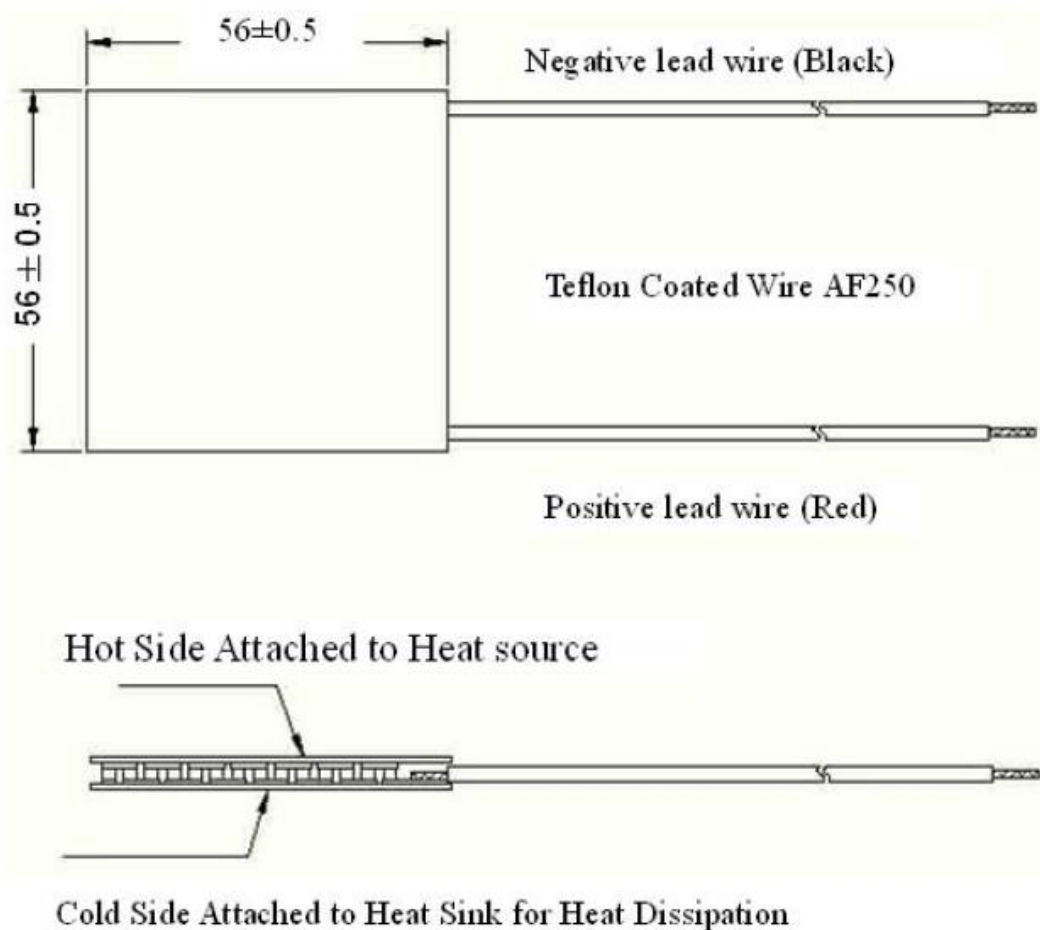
Габаритный чертёж ТЭМ TEG1-24111-6.0
